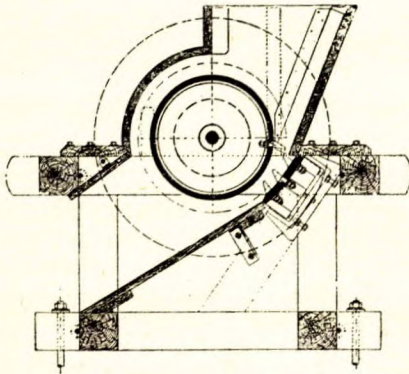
Désintégrateur à pouvoir moteur de Abjorn Anderson's pour mousse litière.
